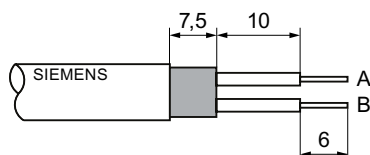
Préparation des extrémités de câble pour le montage du connecteur de bus à départ de câble axial
